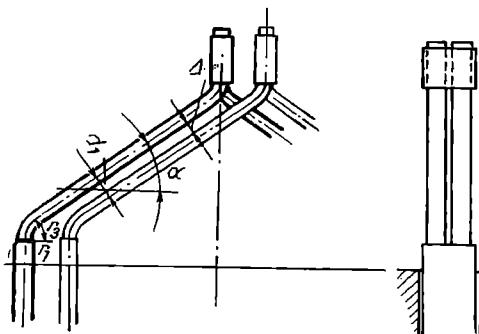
Dimensiunile capului de bobină de înfășurare de curent alternativ, realizată cu conductor dreptunghiular și așezată în rotor.
